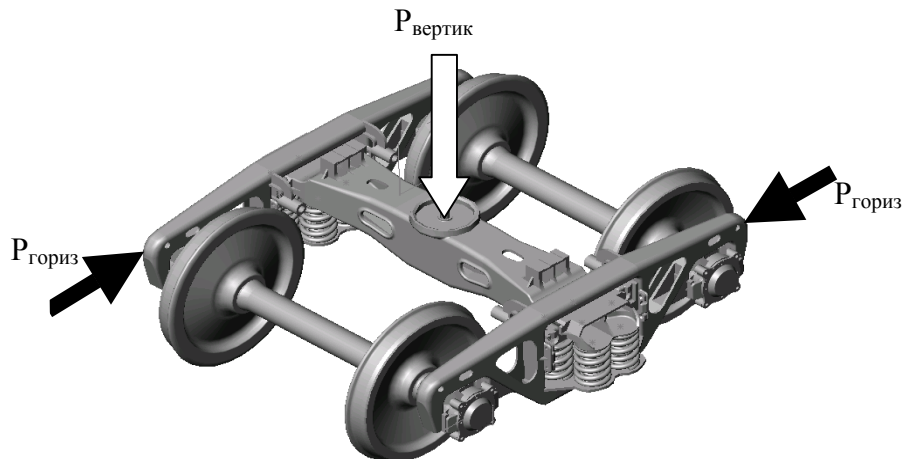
Схема приложения нагрузок при испытаниях для исследования силовых связей в горизонтальной плоскости
